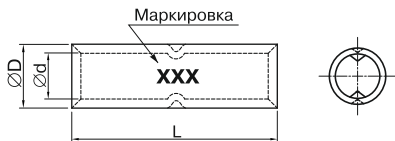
Гильзы медно-алюминиевые, внешний вид и габаритные размеры
